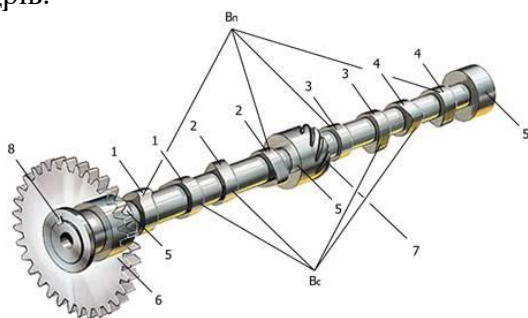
Розподільний вал чотирициліндрового двигуна: 1, 2, 3, 4 – кулачки (Вп – впускні, Вс – випускні); 5 – опори; 6 – шестерня приводу розподільного валу; 7 – шестерня приводу масляного насосу; 8 – шпонка
